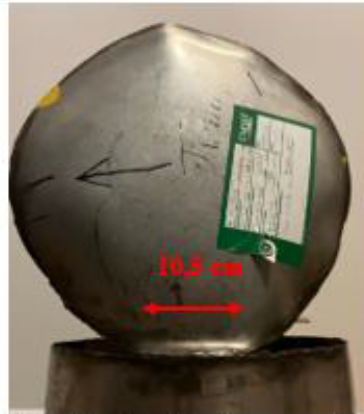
Soudure du couvercle ayant résisté
